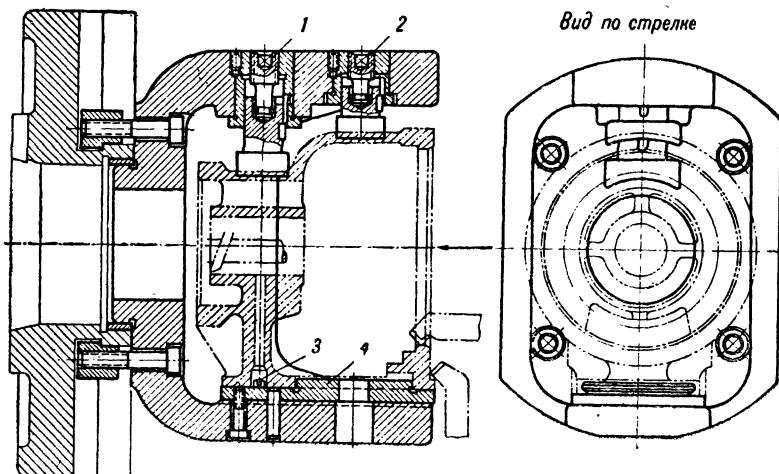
Установочно-зажимное приспособление для обработки изделия коробчатой формы.
